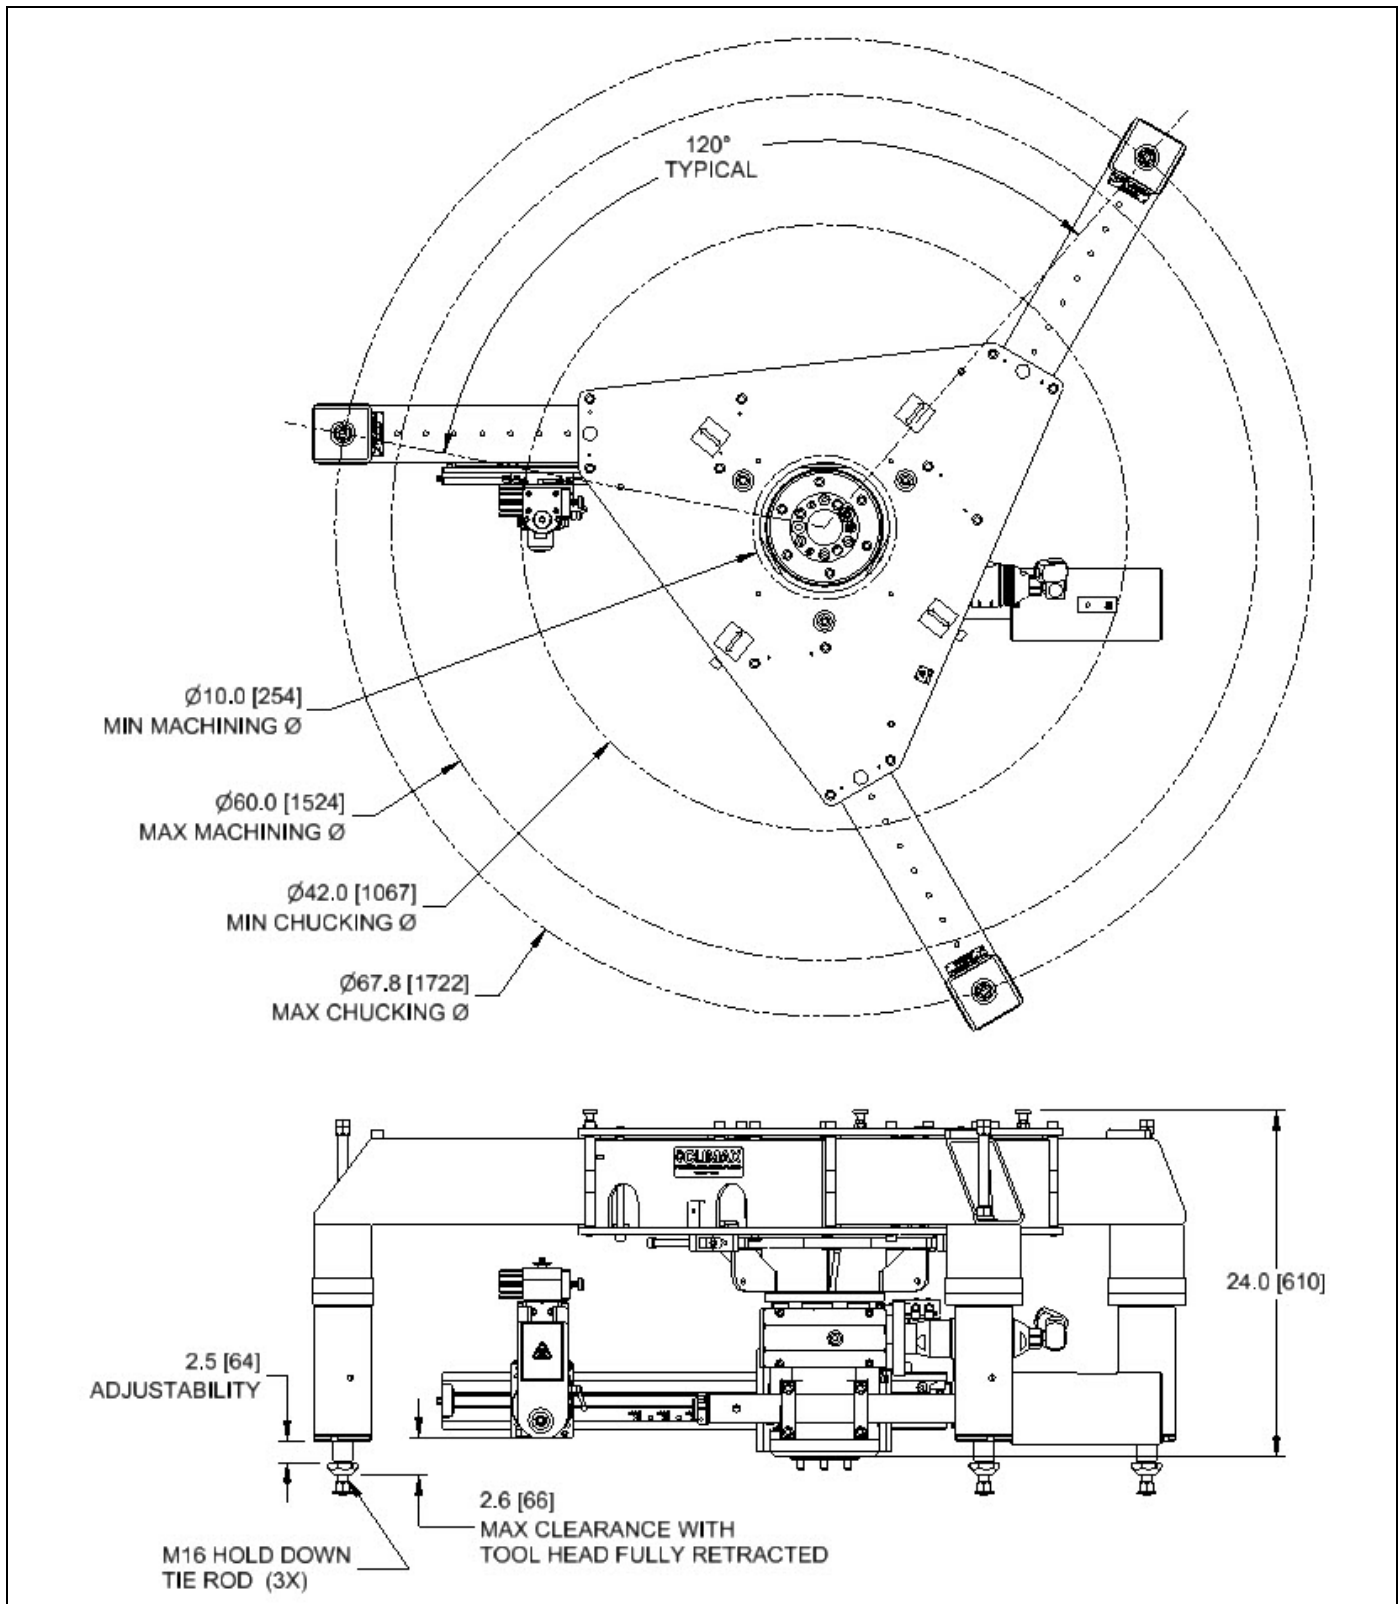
FF6300 DIMENSIONS DE L'ENSEMBLE DE MONTAGE DE
